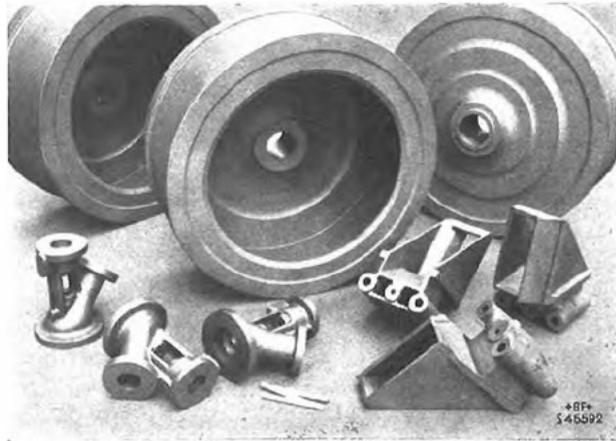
Zentrifugentrommeln, Schälmesserhalter, Ventilgehäuse in korrosionsbeständigem Stahlguß 18/8
